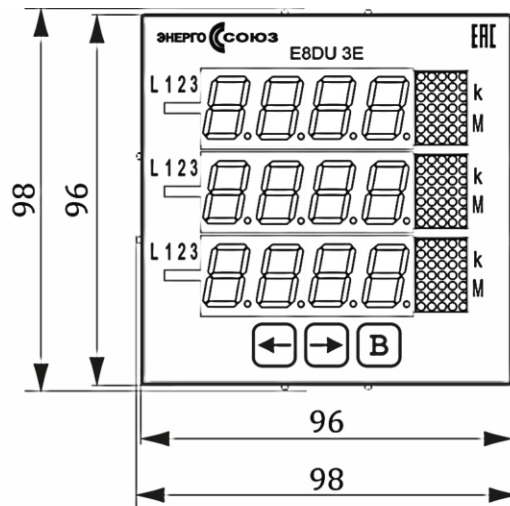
Габаритные и установочные размеры внешнего трехстрочного показывающего устройства E8DU 3E
